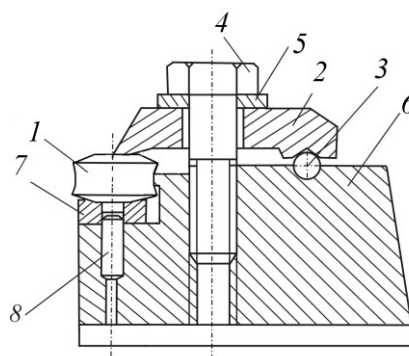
Конструкция резцовой державки: 1 – режущая пластина; 2 – прижим; 3 – опорный шарик; 4 – винт; 5 – шайба; 6 – корпус; 7 – сепаратор; 8 – штифт
